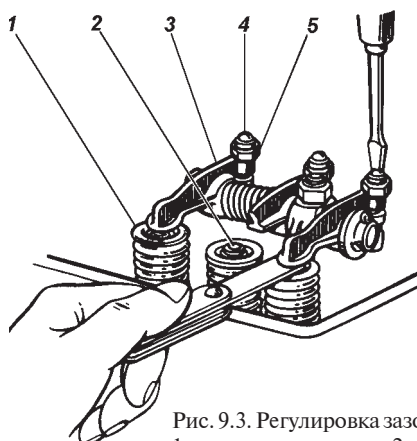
Регулировка зазора между коромыслом и клапаном: 1 -тарелка пружины; 2 -клапан; 3 -коромысло; 4 -регулирующий винт; 5 -контргайка
